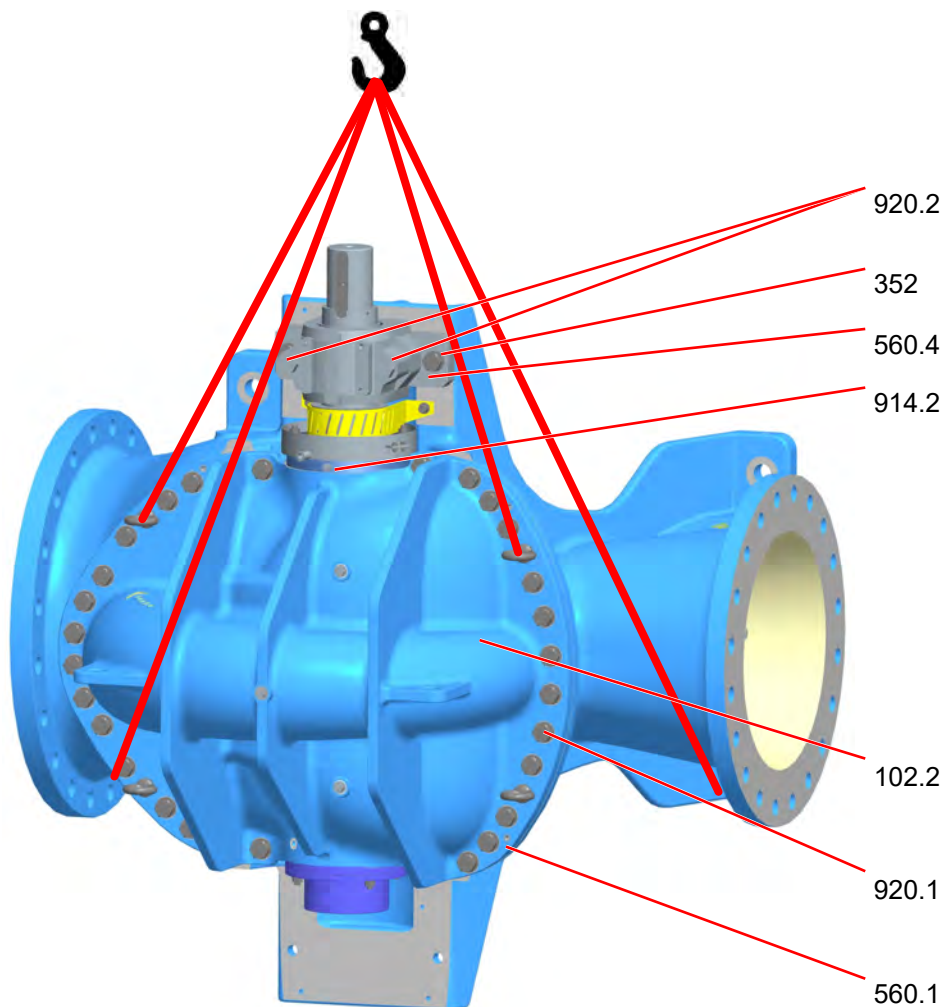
Демонтаж верхней части корпуса — ASP-V
